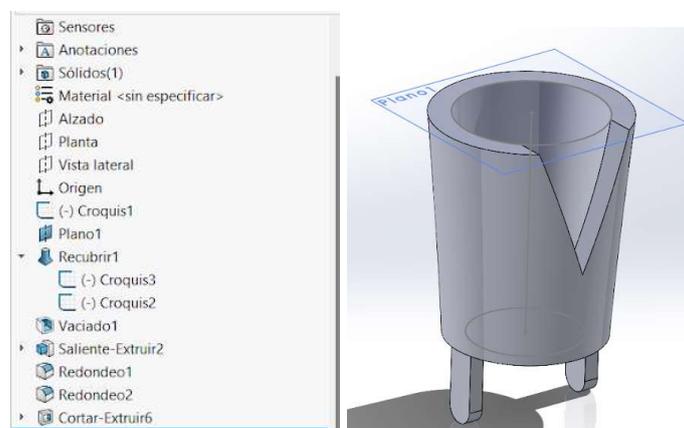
Captura de pantalla SolidWorks, herramienta cortar 1.1. Elaboración propia.
